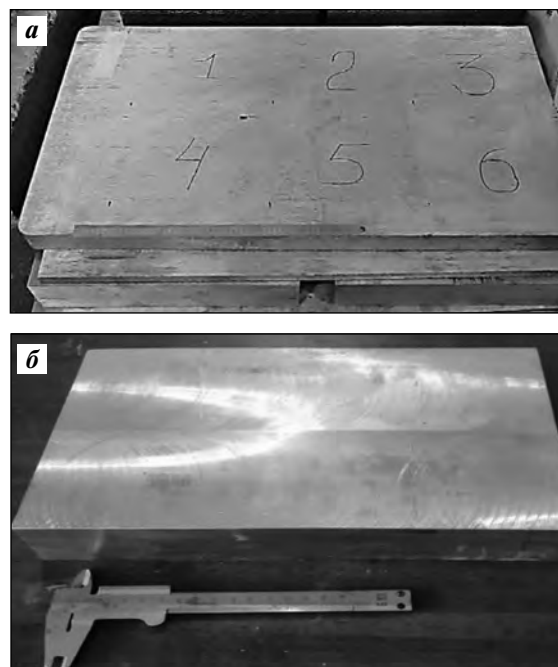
Внешний вид темплета, вырезанного из промышленного крупногабаритного слитка (а), и заготовки для листовой прокатки (б) из сплава 1580
